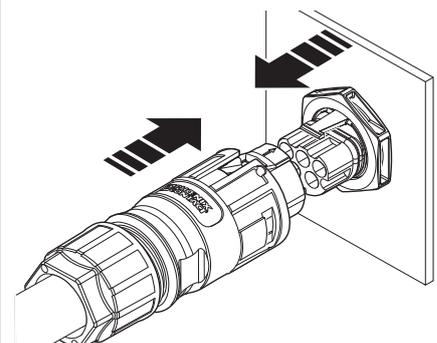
AC-Anschlussstecker mit dem Gerätesteckverbinder einrasten.
